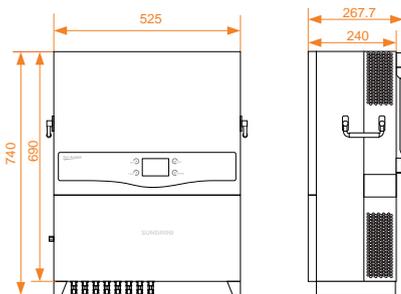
O Fig. 2-3 Dimensões externas do inversor (em mm)
